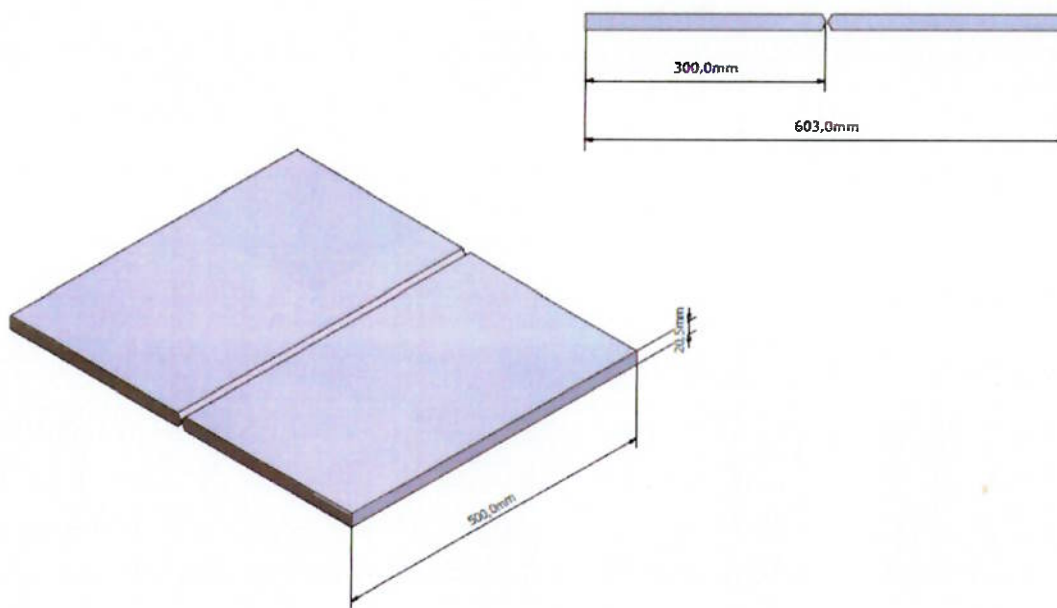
Detalhes das chapas chanfradas e montadas antes da execução da soldagem.
